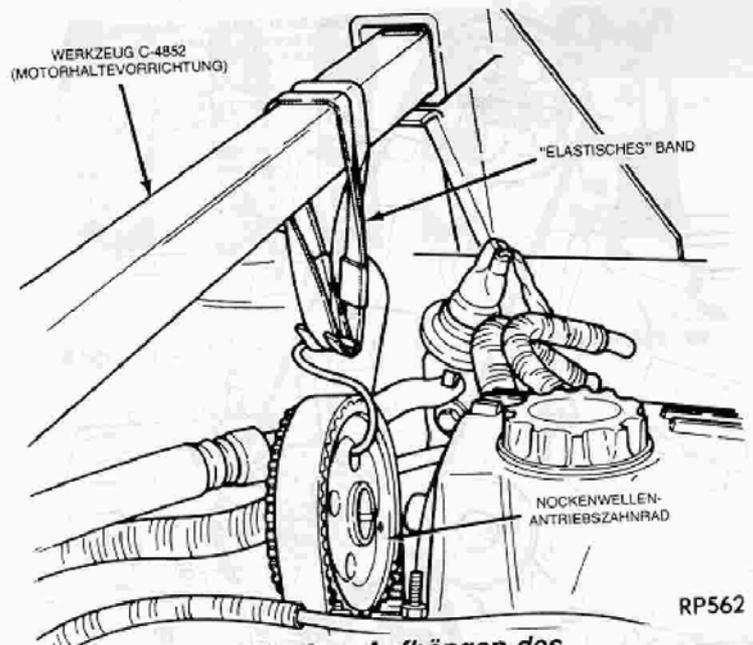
Aufhängen des Nockenwellen-Antriebszahnades
